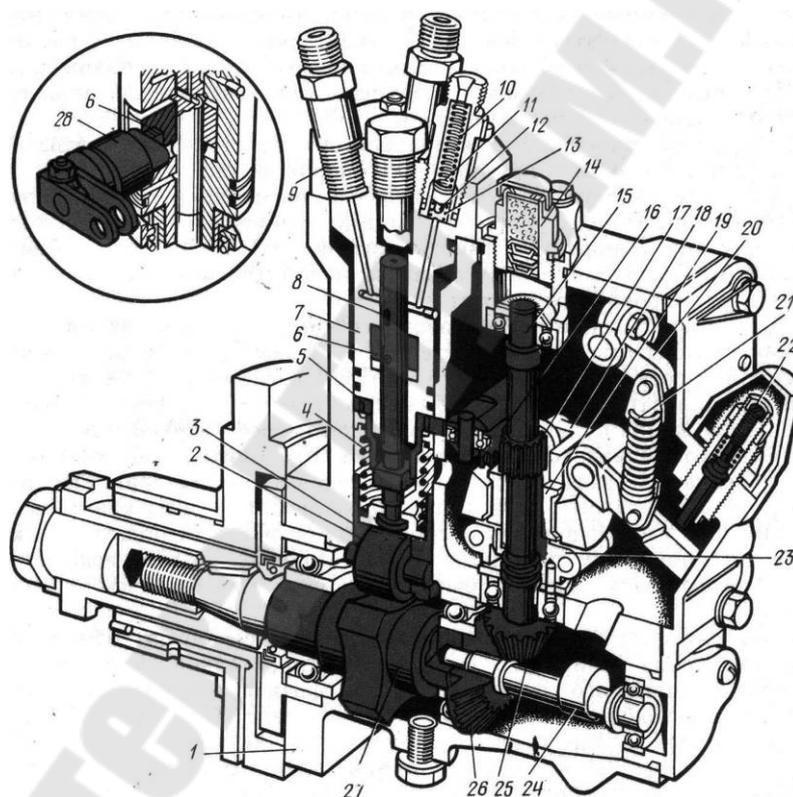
Топливный насос НД-21/4 с регулятором:
